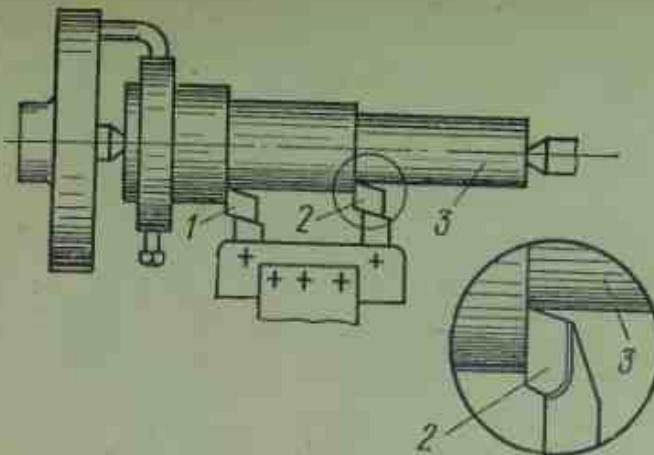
Установка заготовки в центрах для подрезки двух уступов:
